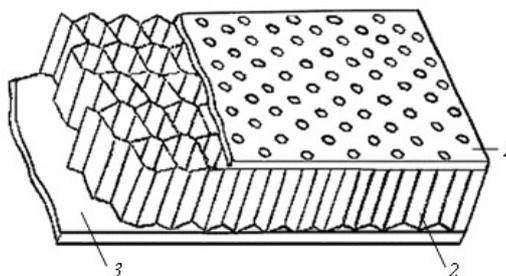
Схематичное изображение однослойной звукопоглощающей конструкции [5]:
